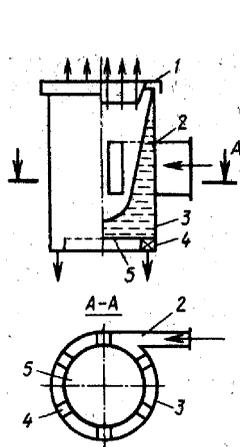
Внутрибарабанный циклон: 1 – крышка; 2 – подводящий патрубок; 3 – цилиндрический корпус; 4 – направляющие лопатки; 5 – доньшко
